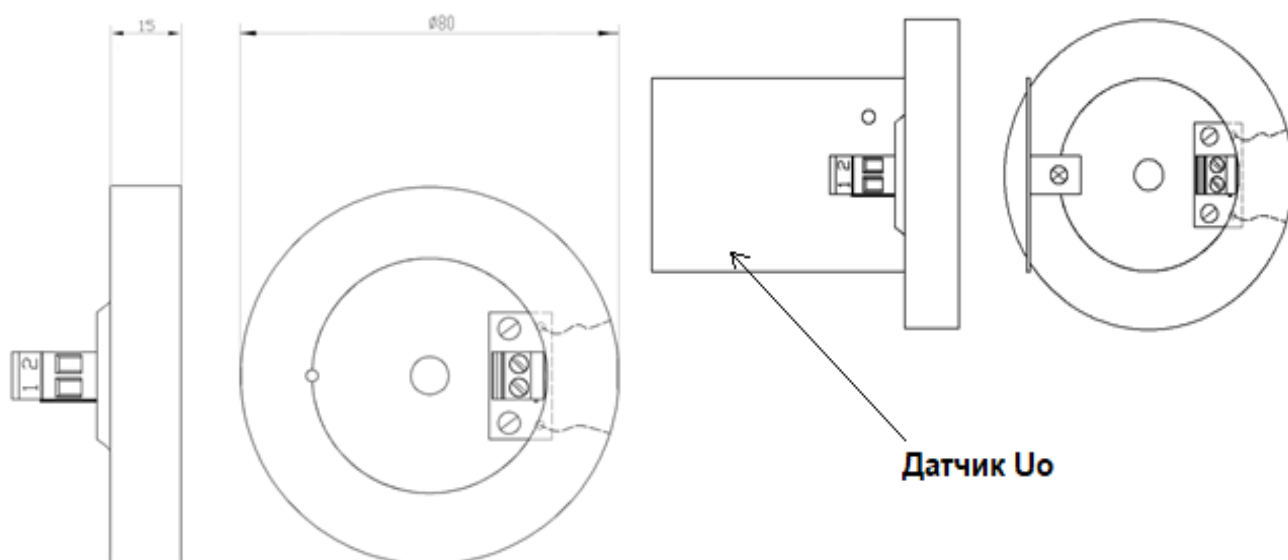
Габаритный чертеж датчика магнитного (ДМ) ИТКЗ-01 (с датчиком Uo)
